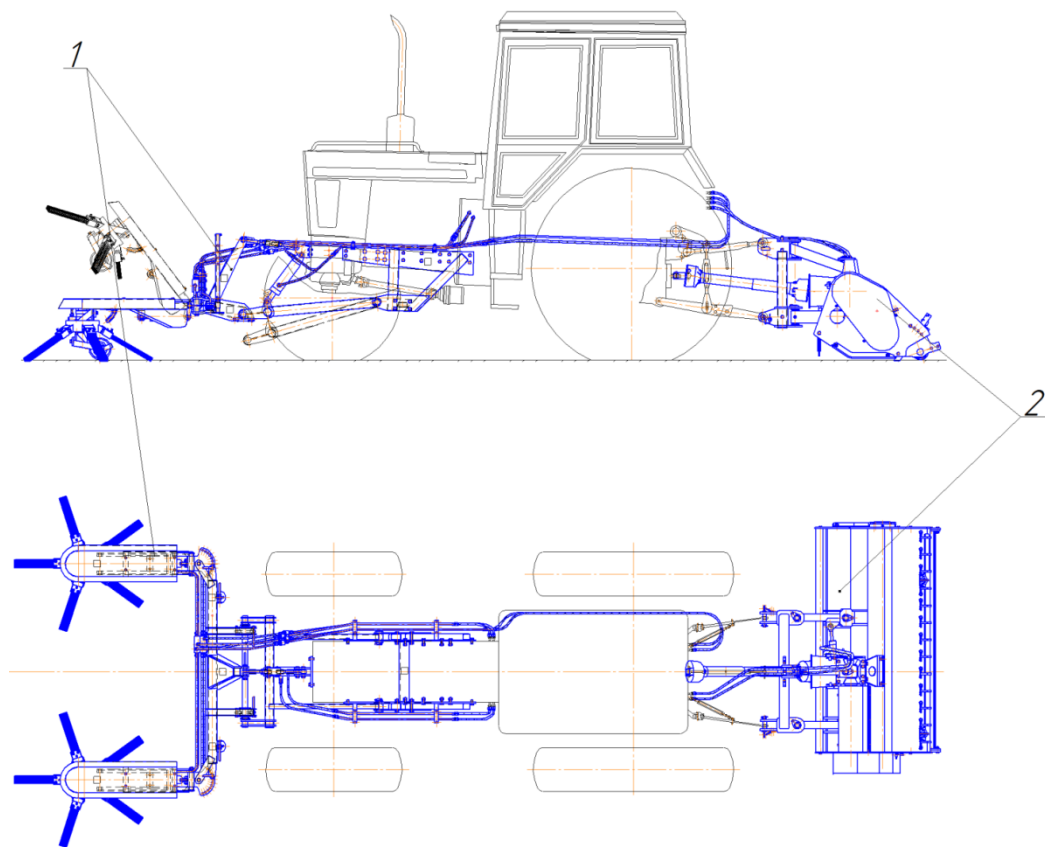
Схема размещения валкователя и измельчителя на тракторе
